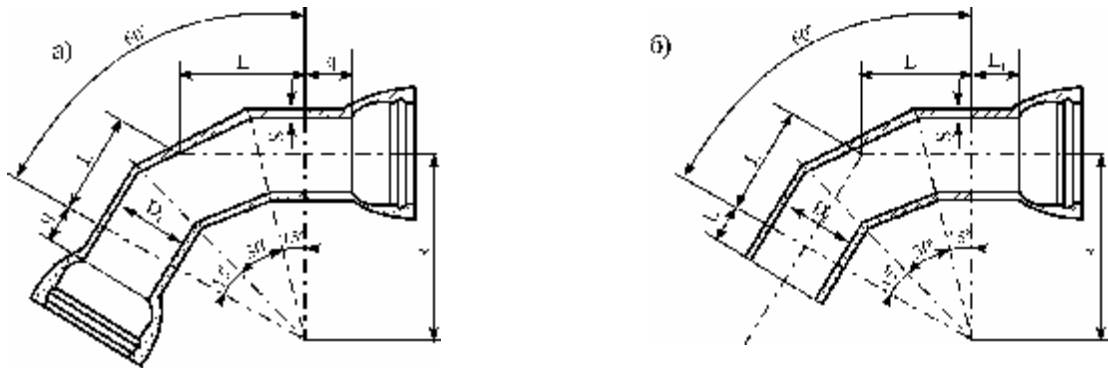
Схема сварных отводов из высокопрочного чугуна на угол 60 град.
